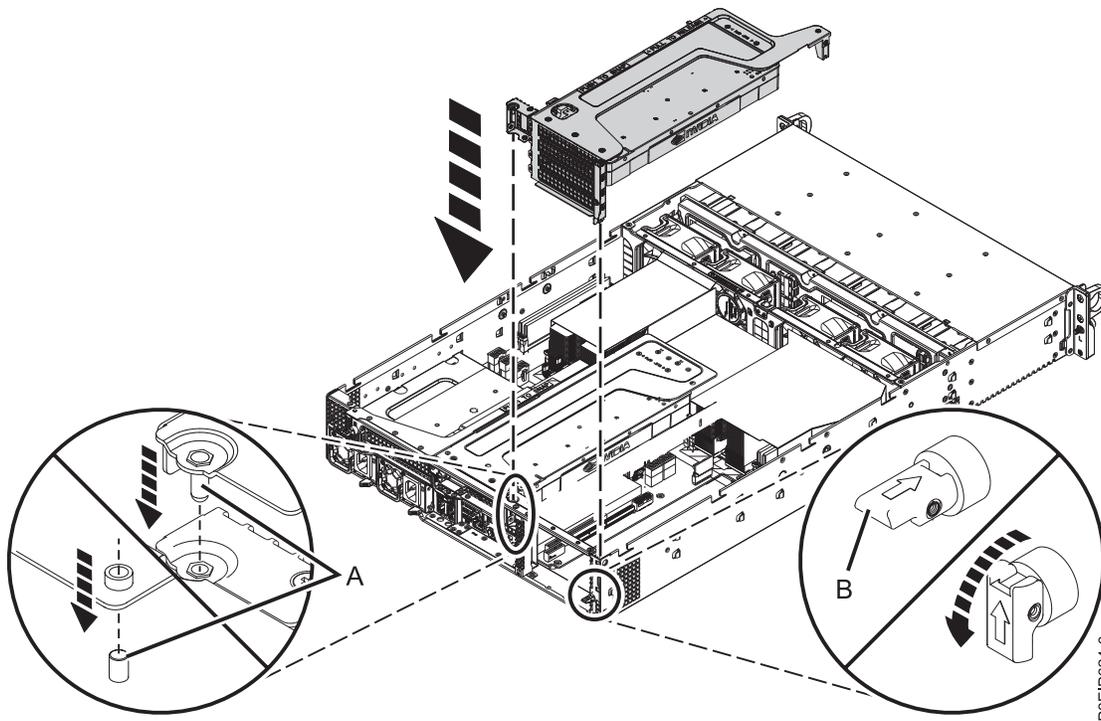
Inserción de la tarjeta de expansión del adaptador PCIe
